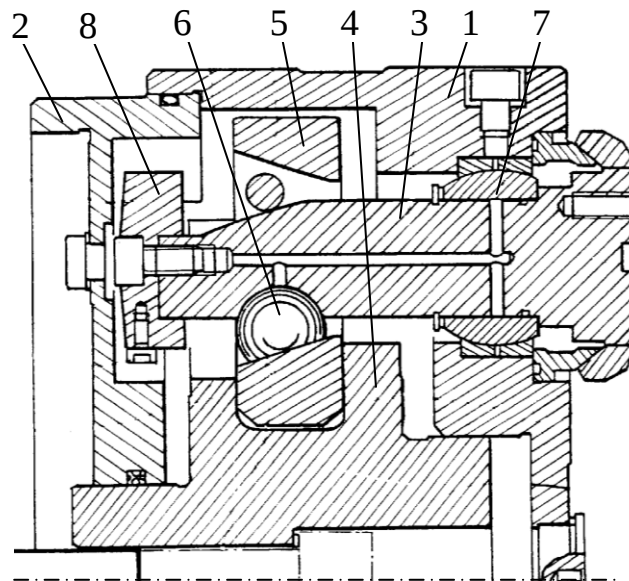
Клино-важільний токарний патрон з компенсацією відцентрових сил контрвантажами, запатентований фірмою Sandvik Tobler
